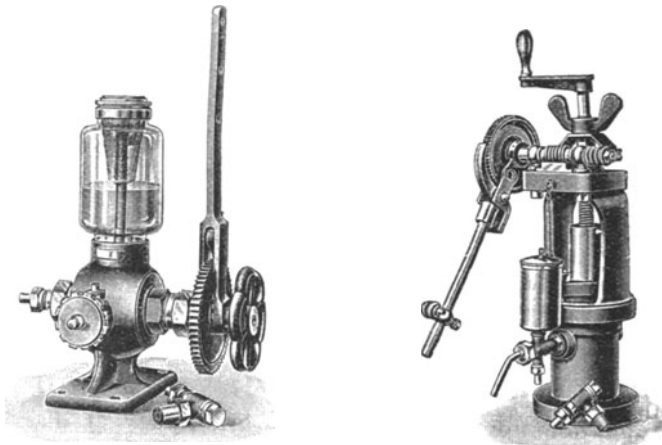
und 124. Schmierpumpe und Schmierpresse für Dampfzylinder von Schäffer und Budenberg.
